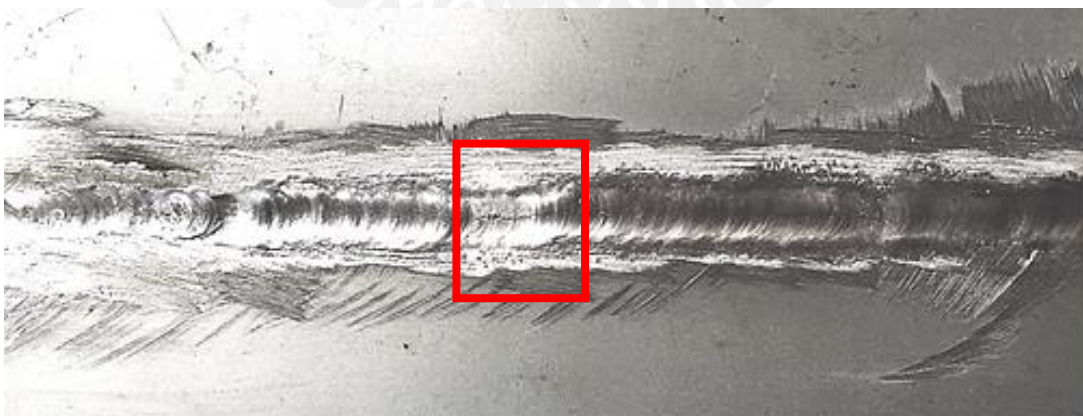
Fisuración en caliente en una soldadura sin aporte
